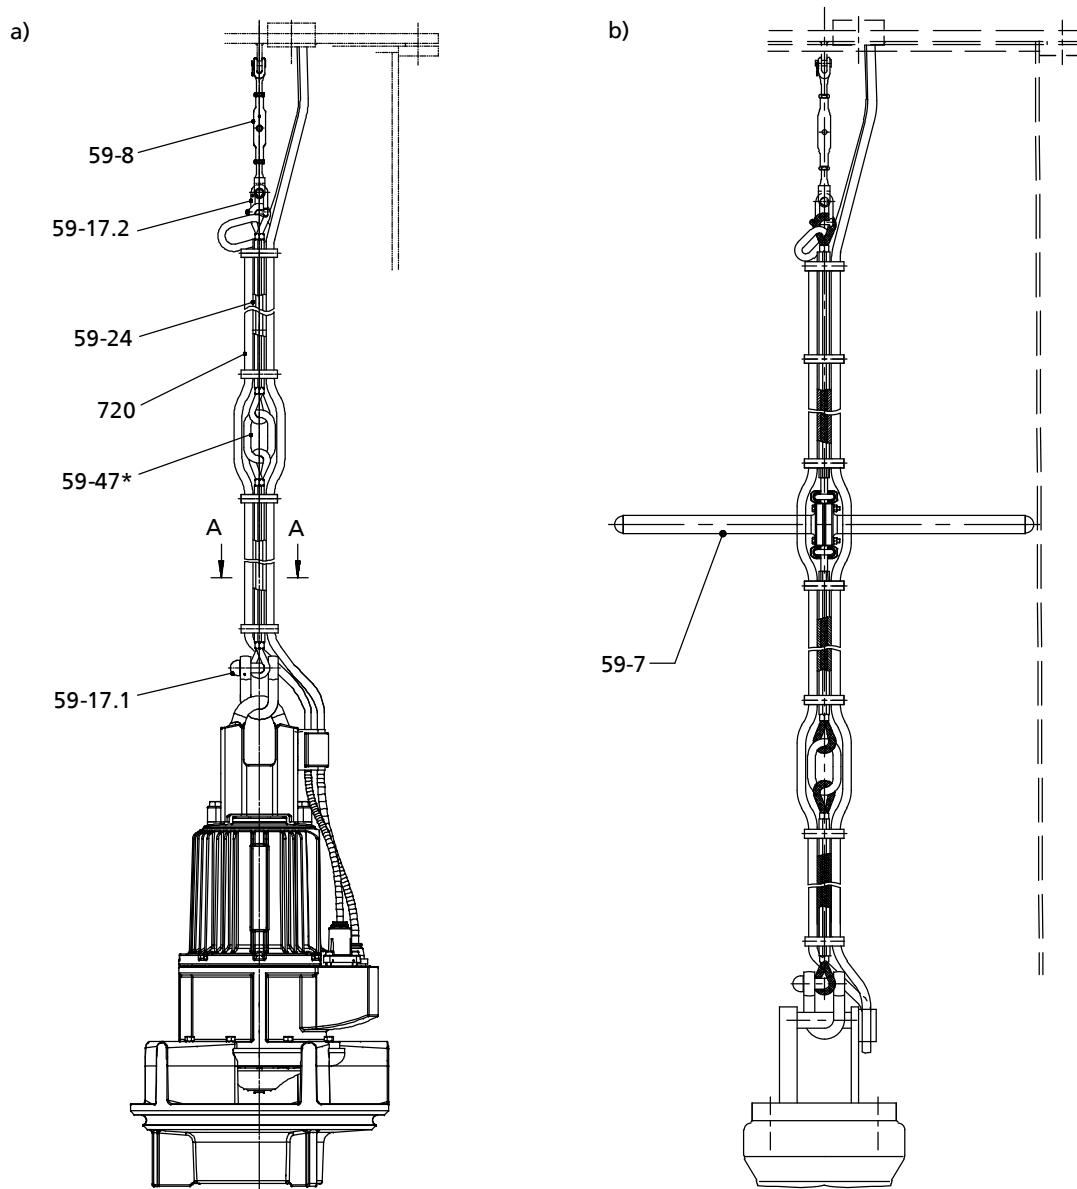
a) Pumpenaggregat mit Tragseil und Spannschloss im Rohrschacht b) Pumpenaggregat mit Tragseil und Spannschloss im Rohrschacht für große Einbautiefen mit Stützkörper
